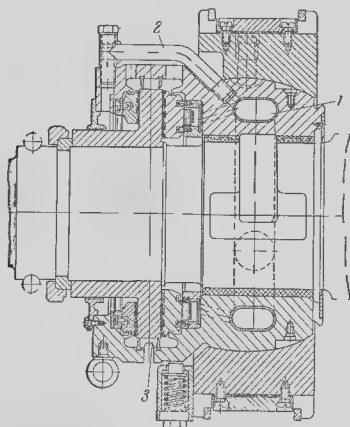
Опорно-упорный подшипник турбины высокого давления ЛМЗ нового типа
